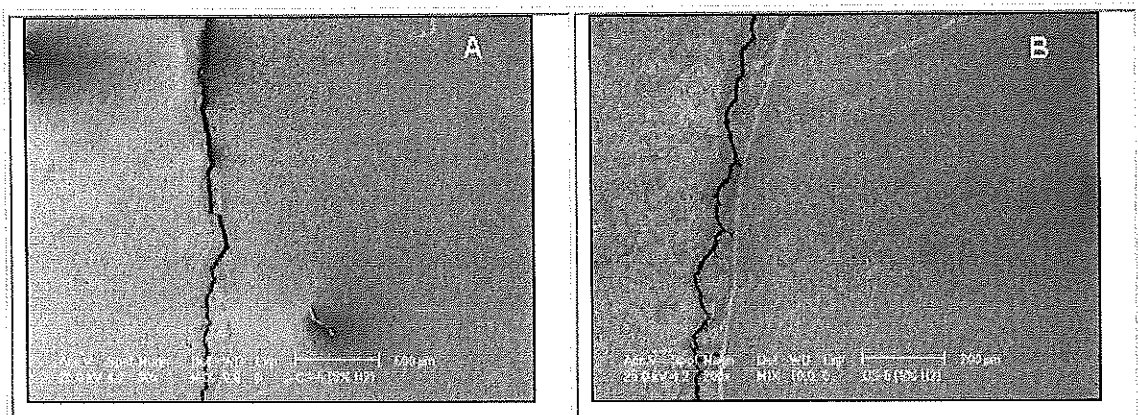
Seguimiento de la fisura de fatiga en el espécimen 5. En esta parte del crecimiento observamos que la grieta se ha internado en la ZAT, junto a la línea de fusión. Ataque: Villella.
